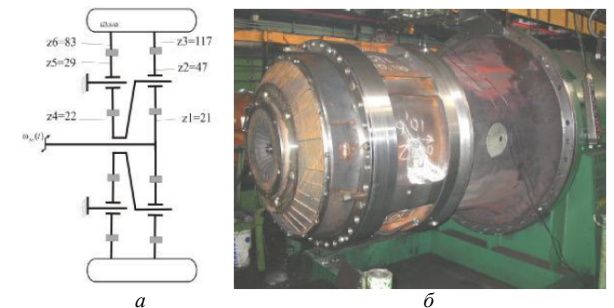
Редуктор мотор-колеса карьерного самосвала БЕЛАЗ:
